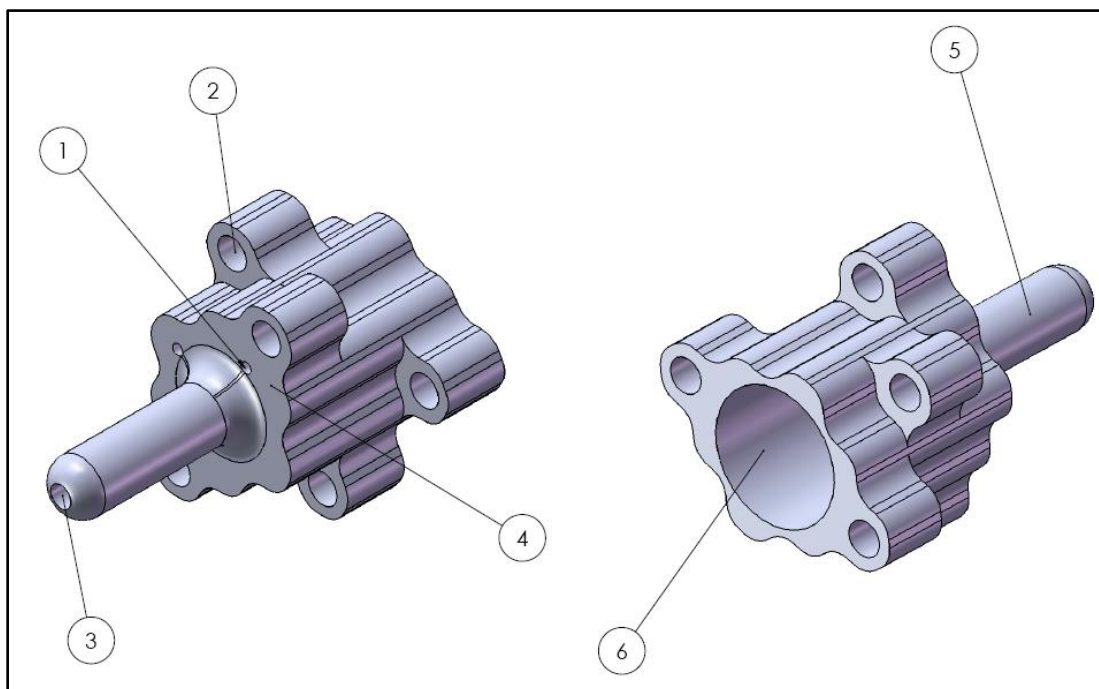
Dispositif de fixation des tubes instrumentés. (a) vue de dessus (b) : vue côté encastrement du tube
